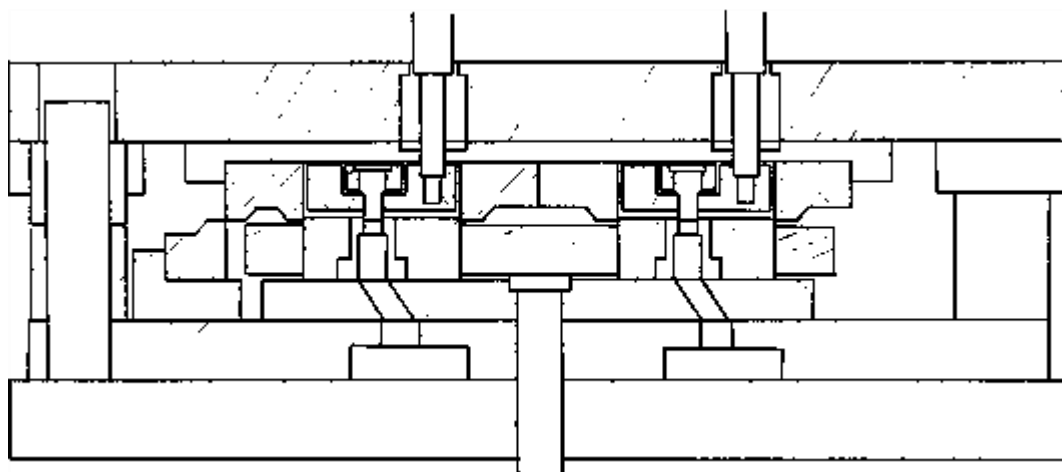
Схема штампа совмещенного действия для вырубки контура деталей и пробивки отверстий с применением однорядного раскроя ленты
